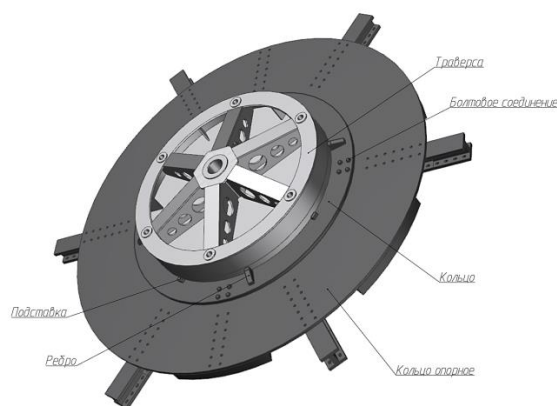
Сборочно-сварочное приспособление для траверсы
